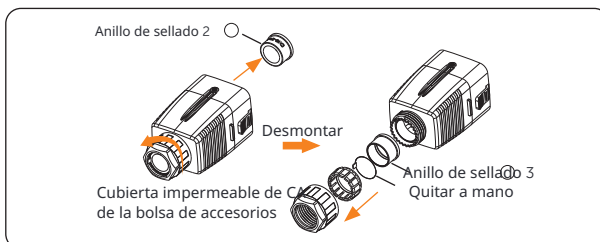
7 Desmontaje de la cubierta impermeable de CA
